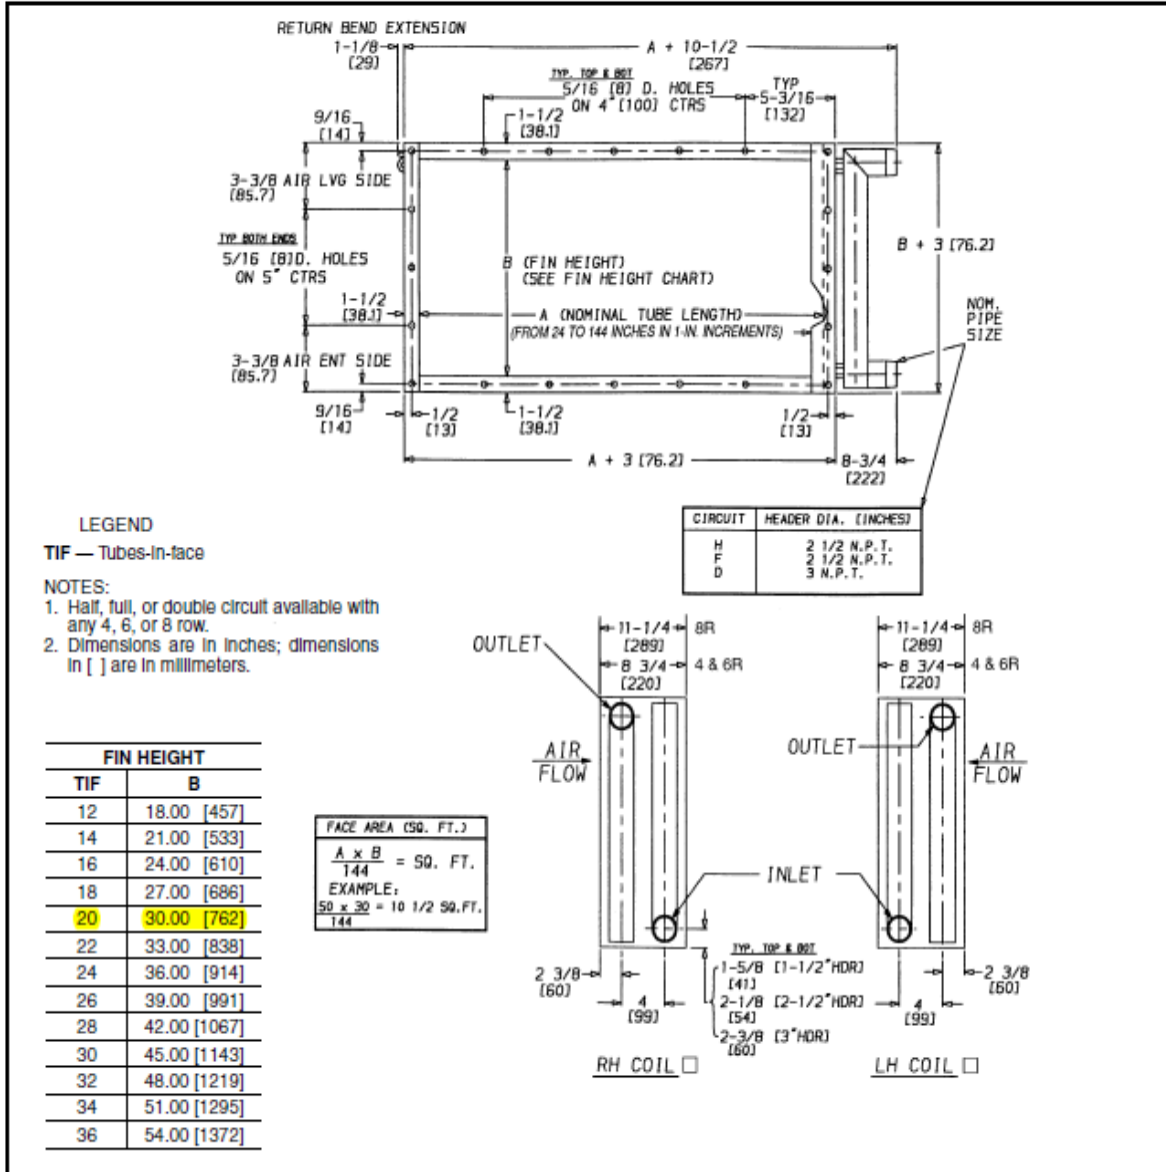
Dimensiones del serpentín de enfriamiento UMA-01
